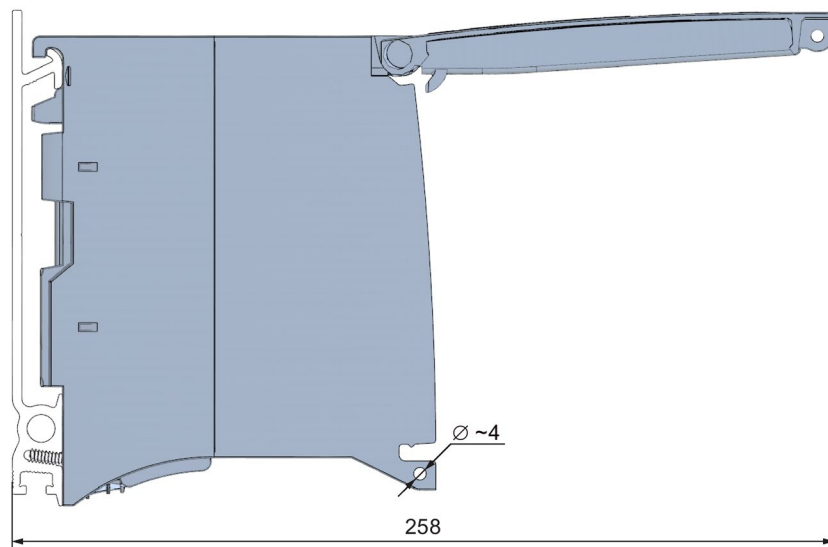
Dessin coté de la CPU 1515-2 PN, vue de côté avec volet frontal ouvert
